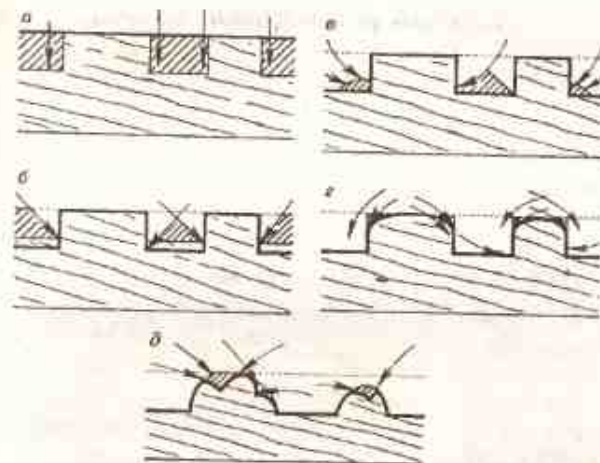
Выполнение глухой рельефной резьбы: а — надрез или обруб по контуру; б — подрезка к основанию надреза; в — выборка фона начерто; г — заovalивание орнамента и зачистка фона; д — разработка рельефа выемками, порезками (стрелками показано направление движения инструмента)
